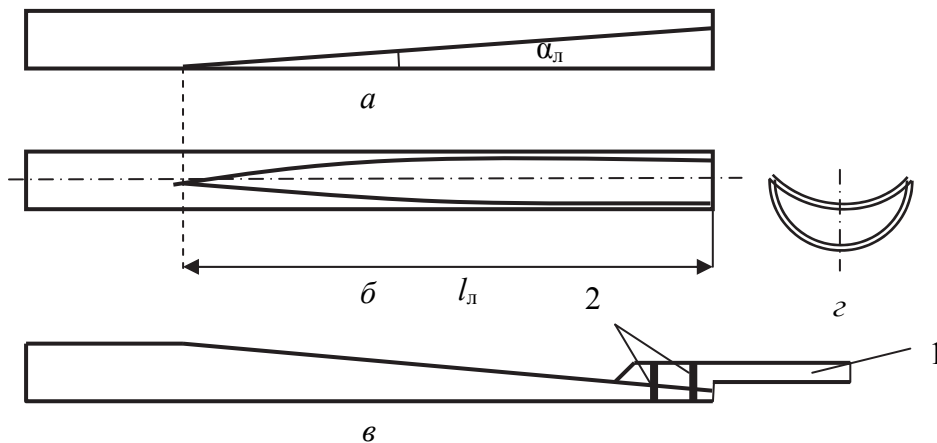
Схемы, поясняющие процесс изготовления стационарного клина: а, б – разметка линии отреза при изготовлении ложка; в – схема клина с установочным патрубком 1 и срезными штифтами 2; г – поперечное сечение ложка клина
